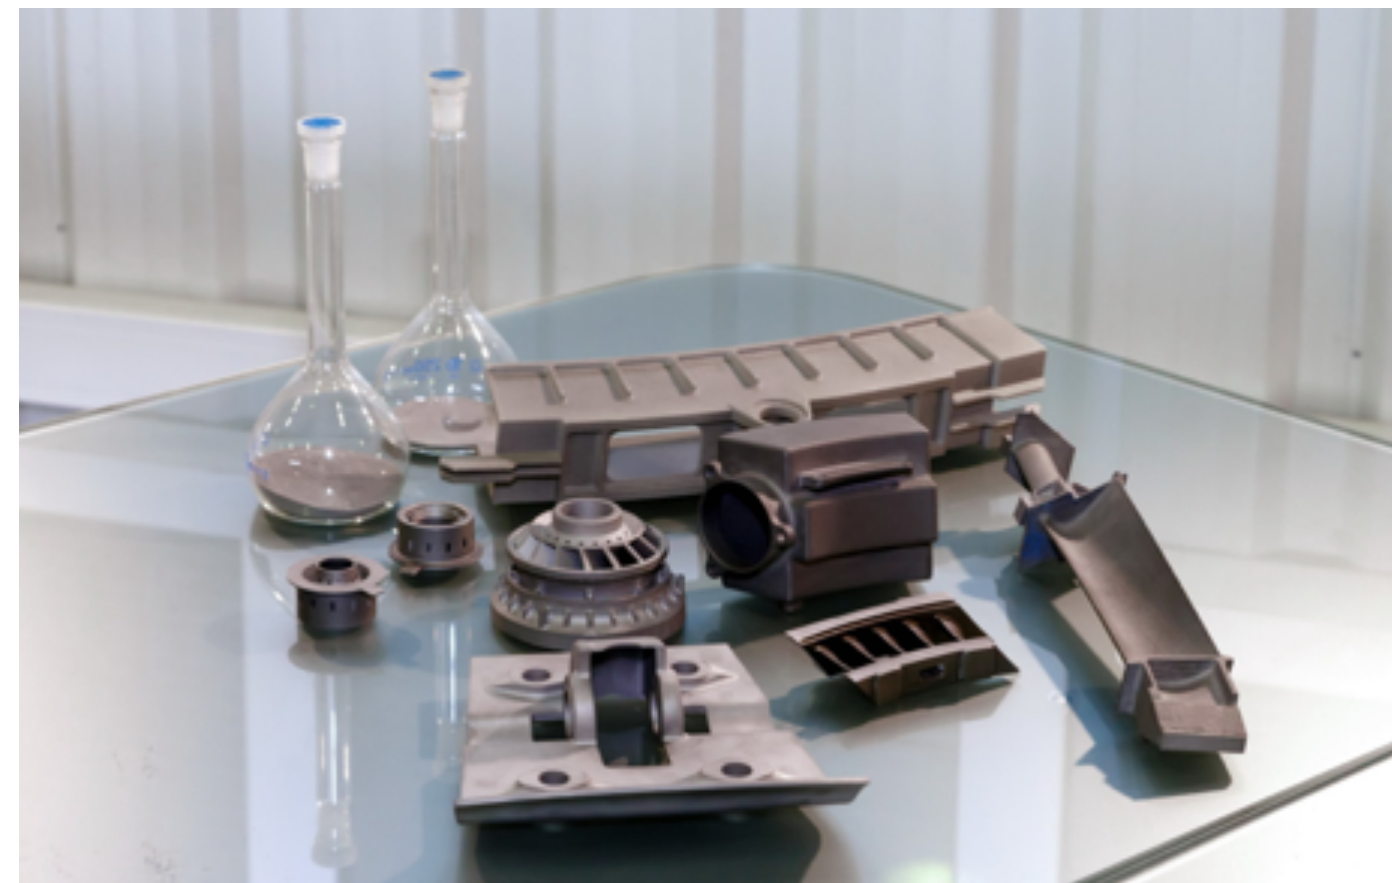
Детали и сборочные единицы газотурбинных двигателей морского назначения
